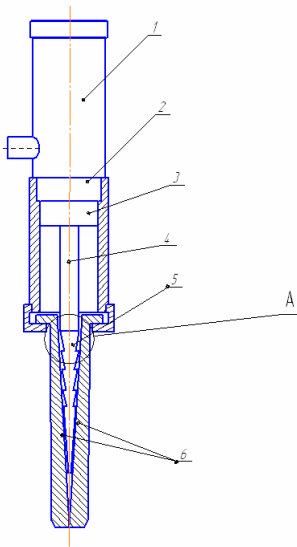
Гидроклиновое рабочее оборудование для реконструкционных работ
